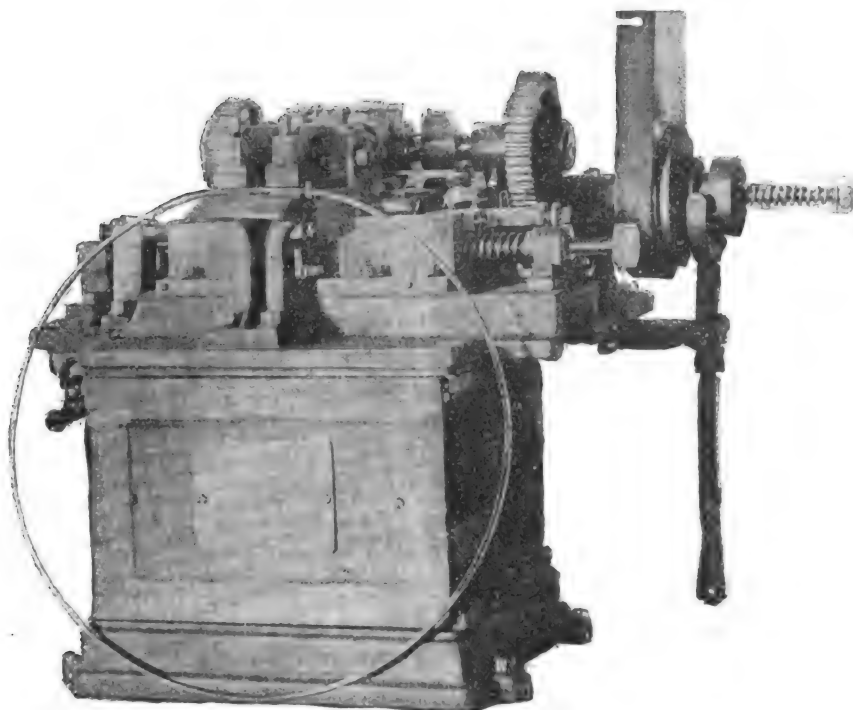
Machine à souder type 2-A, avec commande mécanique.
